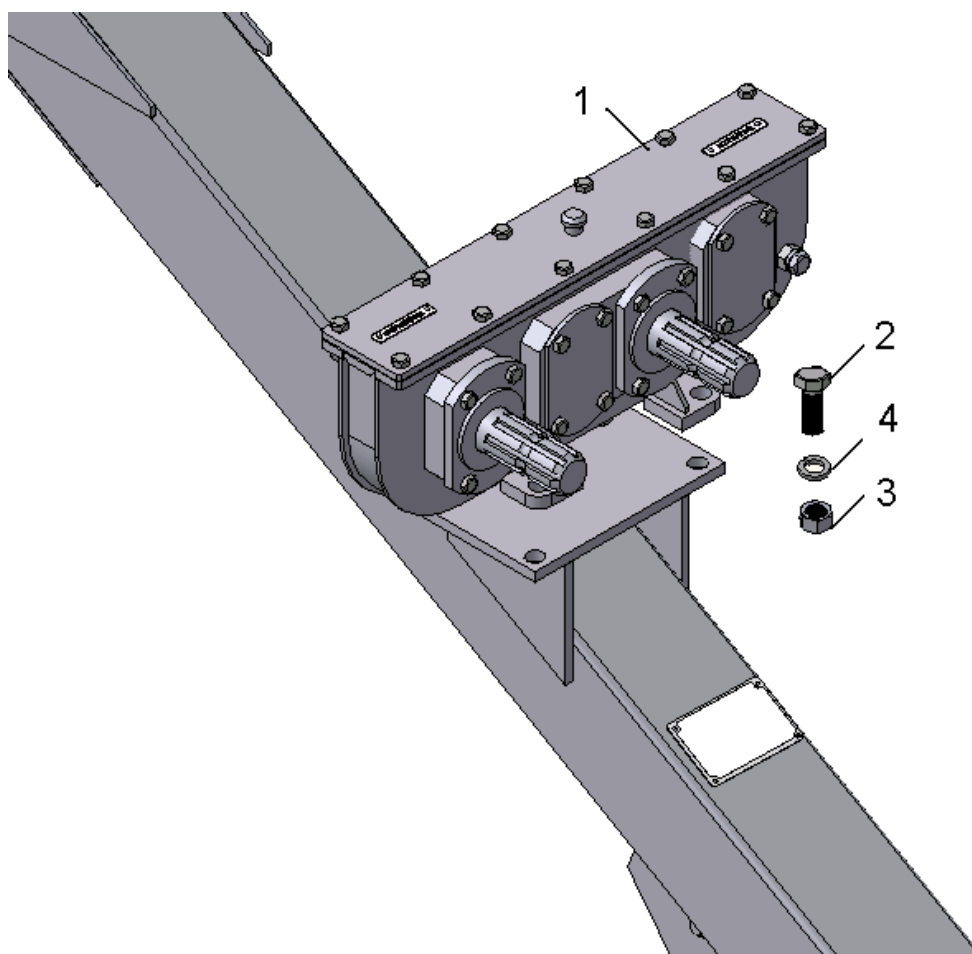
Установка редуктора УГМ-4,2.04.00.000
